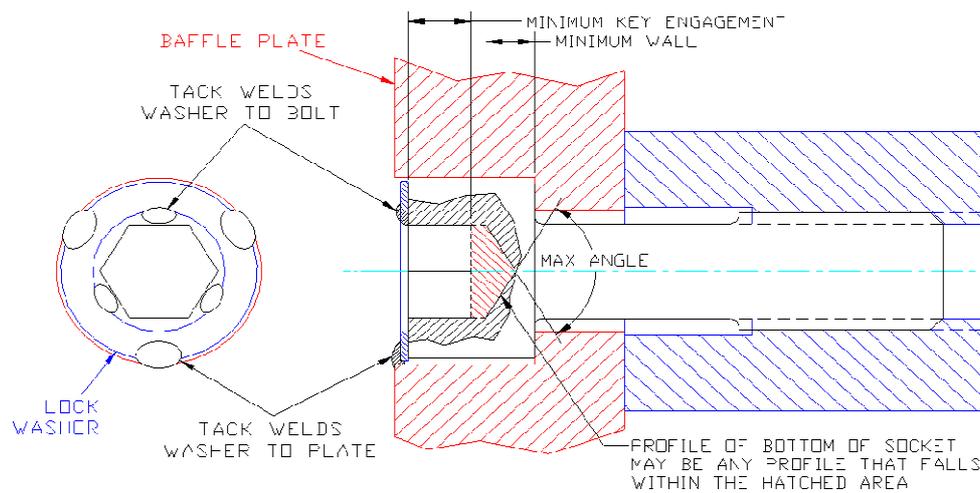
Zeichnung: Einbauzustand einer Innensechskantschraube mit Sicherungsscheibe und Schweißpunktsicherung
